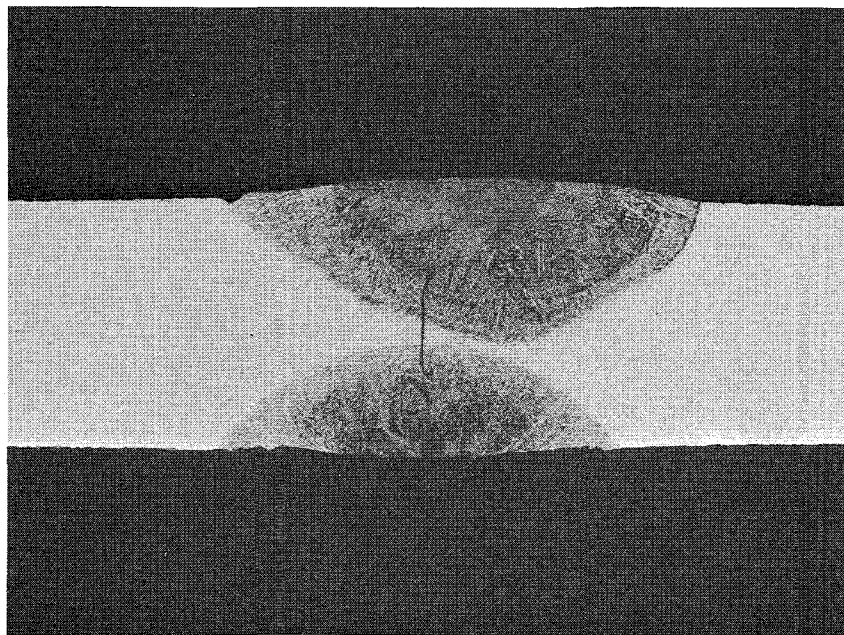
Makroaufnahme vom Querschliff der Schweißnaht bei dem Cr-Ni-Stahl 1.4439 im WS-Zustand (Bindefehler aufgrund nicht entfernter Zunderschichten nach Wärmebehandlung) $V = 10:1$
